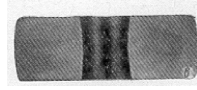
Формоміна товстостінної кінцевої заготовки
